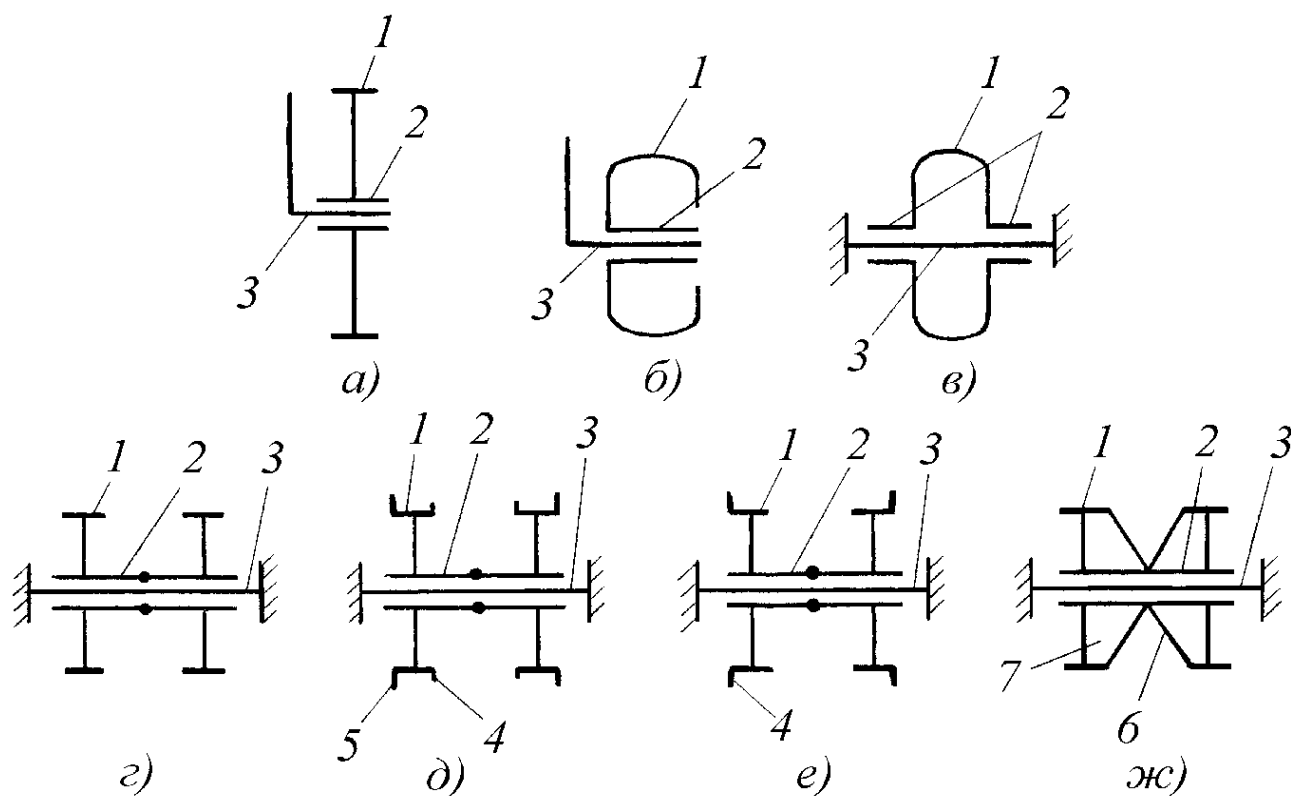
Схеми конструкцій опорних ковзанок [32]: 1 – обід котка; 2 – маточина; 3 – вісь котка; 4, 5 – реборди; 6 – кільцева канавка; 7 – ребро жорсткості
